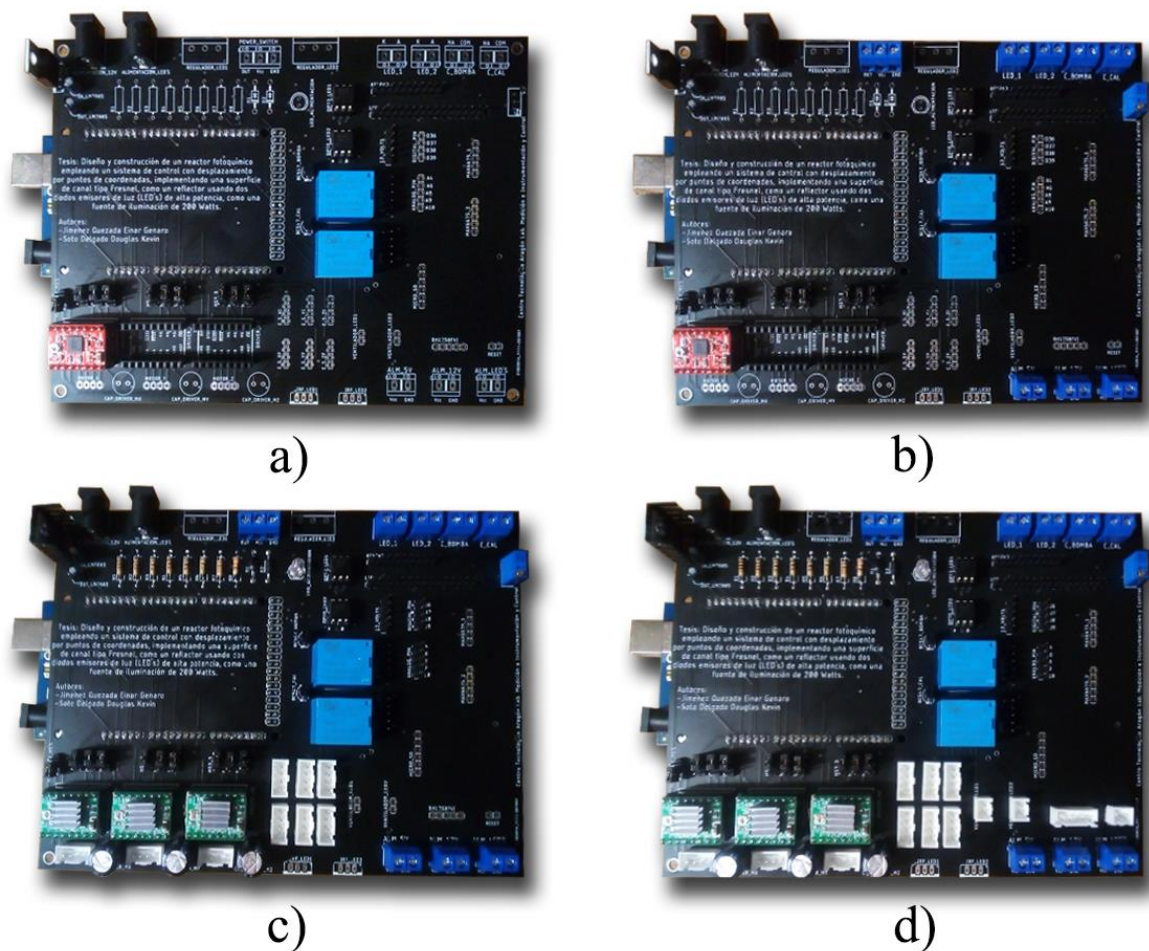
Proceso de montaje y soldado de los componentes en la tarjeta de propósito general.
